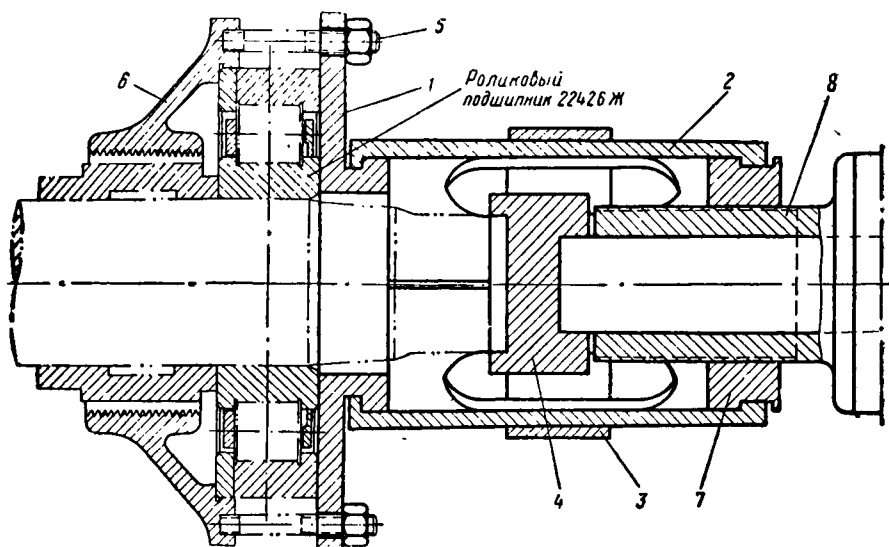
Снятие роликового подшипника с вала якоря тягового двигателя:
